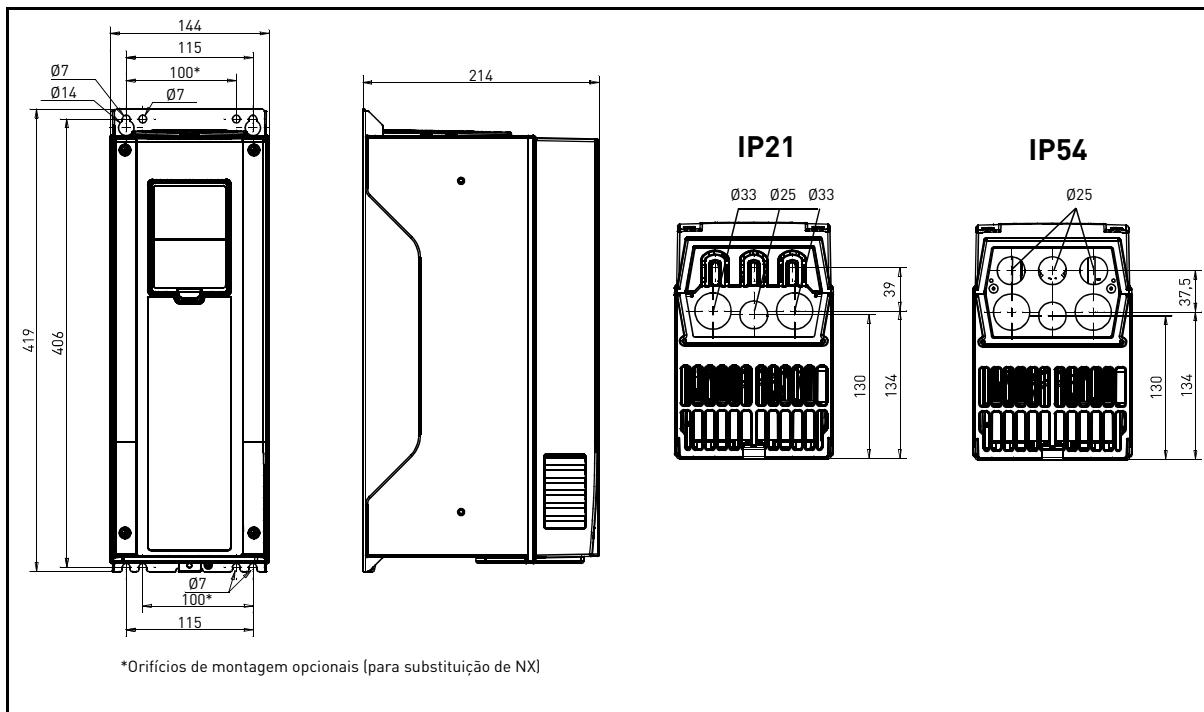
Dimensões do inversor de CA Vacon, MR5, montagem na parede
